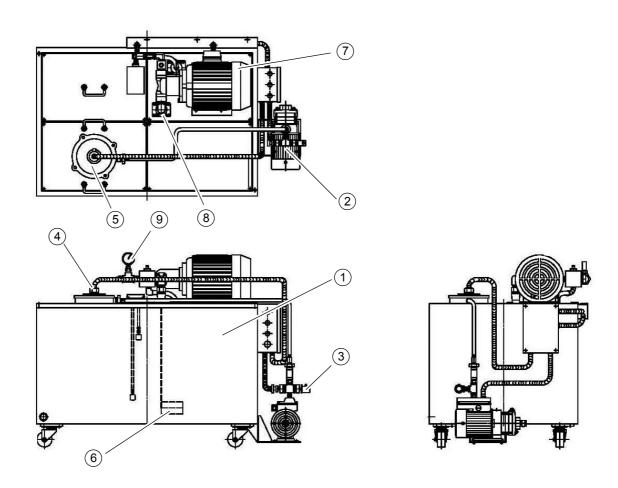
Externes Kühlaggregat 70 bar - External cooling unit 70 bar
